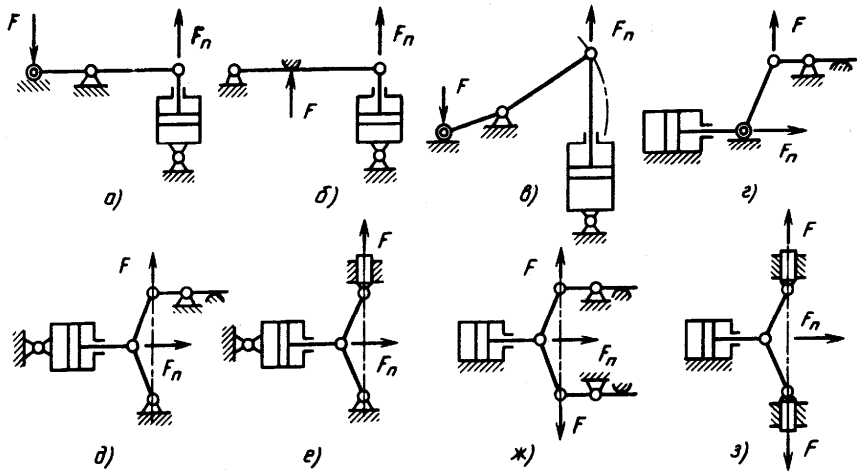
Кинематические схемы рычажных механических усилителей к приводам сборочно-зажимных устройств
